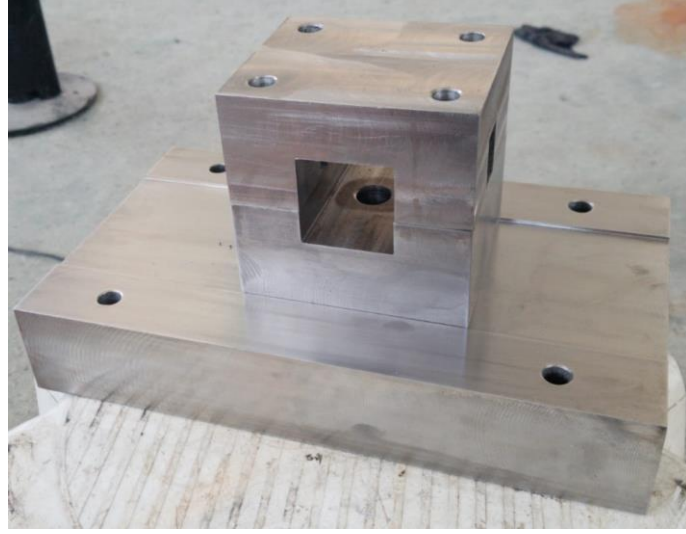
Düzenleme öncesi sürtünme kaynak makinası [5]
